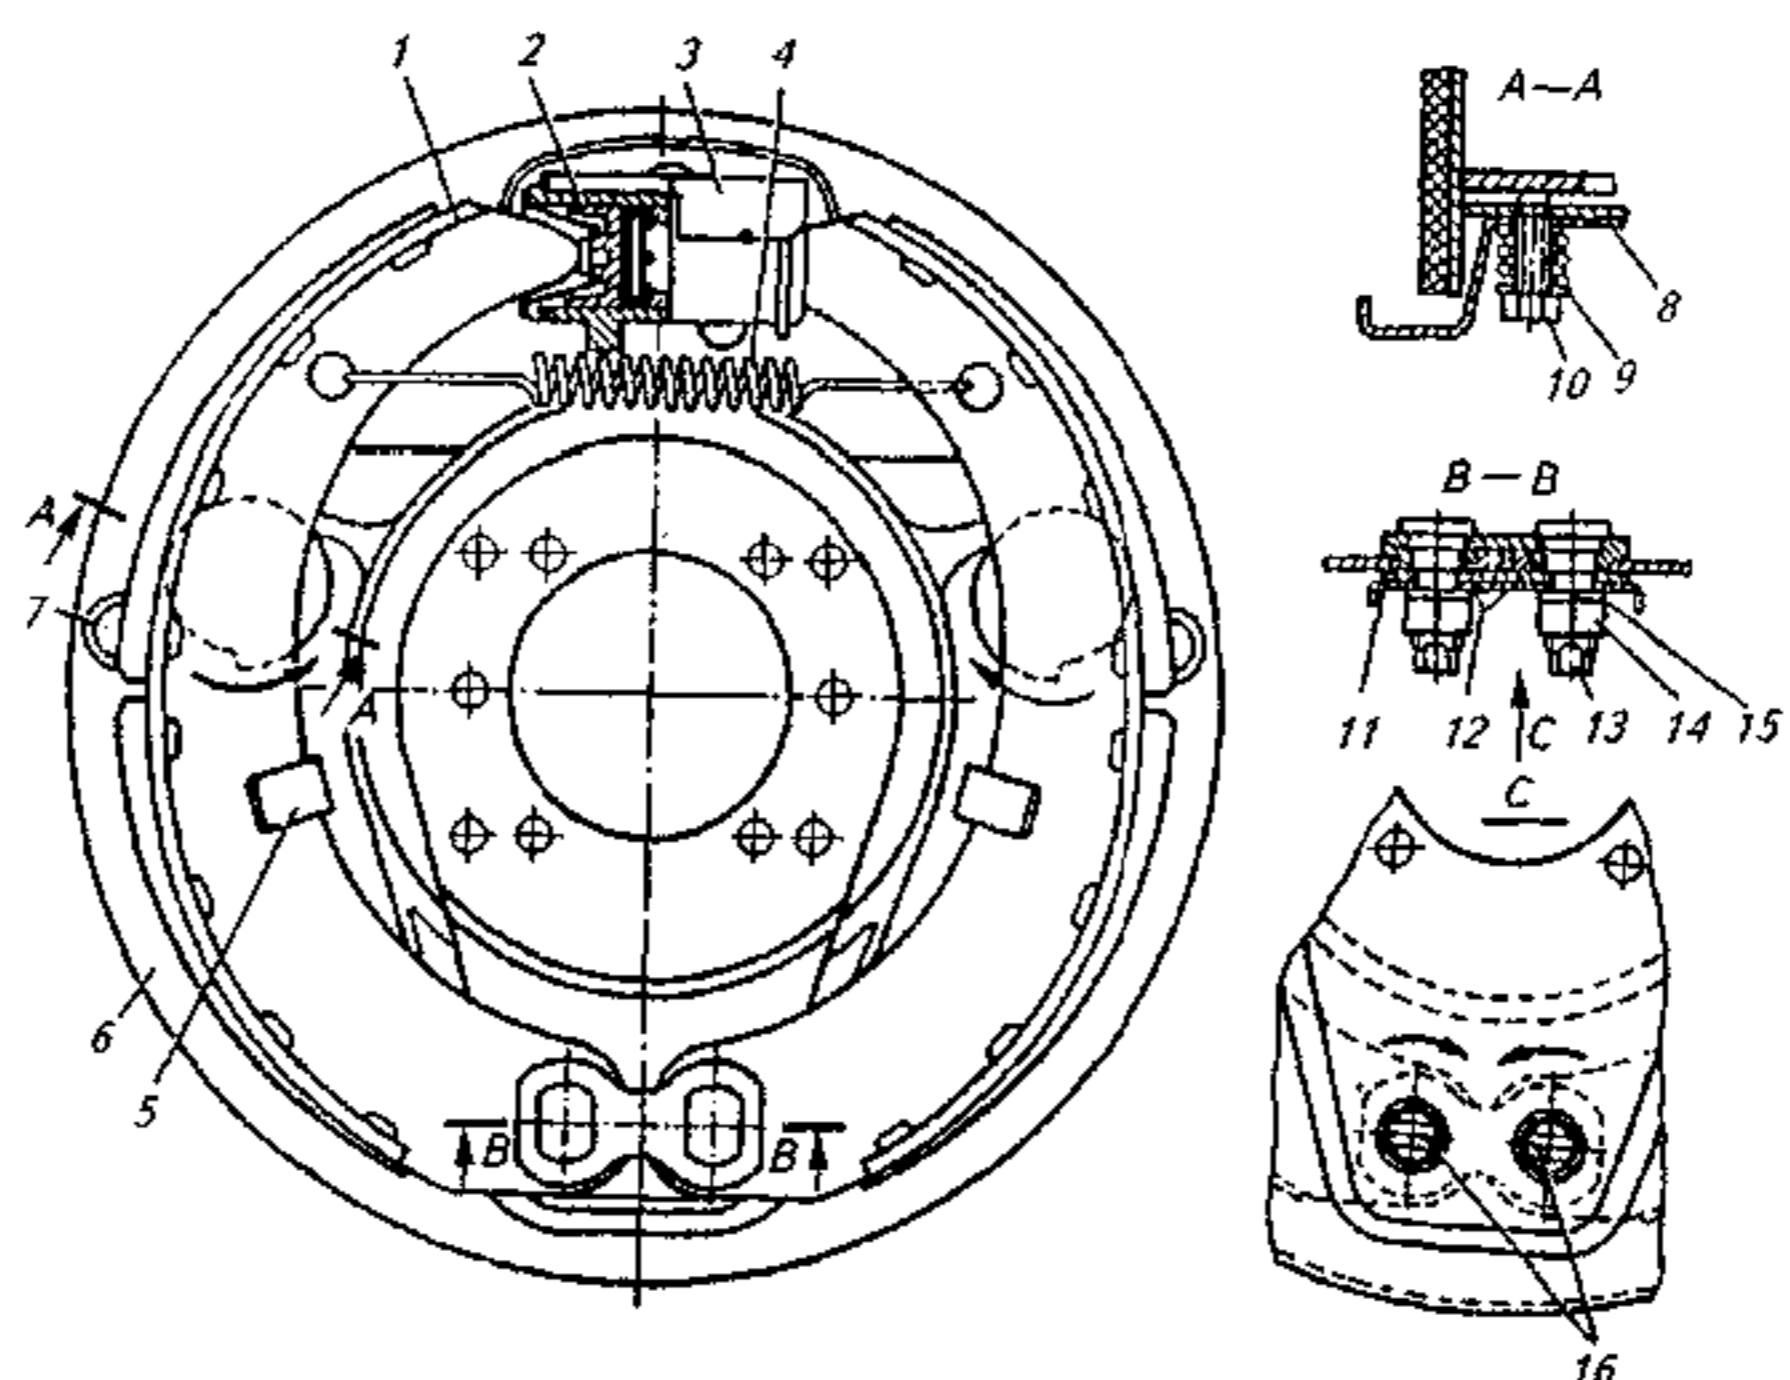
Тормозной механизм автомобиля ГАЗ-53-12: 1 — тормозная колодка; 2 — колесный цилиндр; 3 — экран колесного цилиндра; 4 — возвратная пружина колодок; 5 — направляющая скоба колодок; 6 — тормозной щит; 7 — смотровой люк; 8 — регулировочный эксцентрик; 9 — шайба; 10 — болт регулировочного эксцентрика; 11 — пластина опорных пальцев; 12 — эксцентрики опорных пальцев; 13 — опорный палец тормозной колодки; 14 — гайка; 15 — пружинная шайба; 16 — метки
